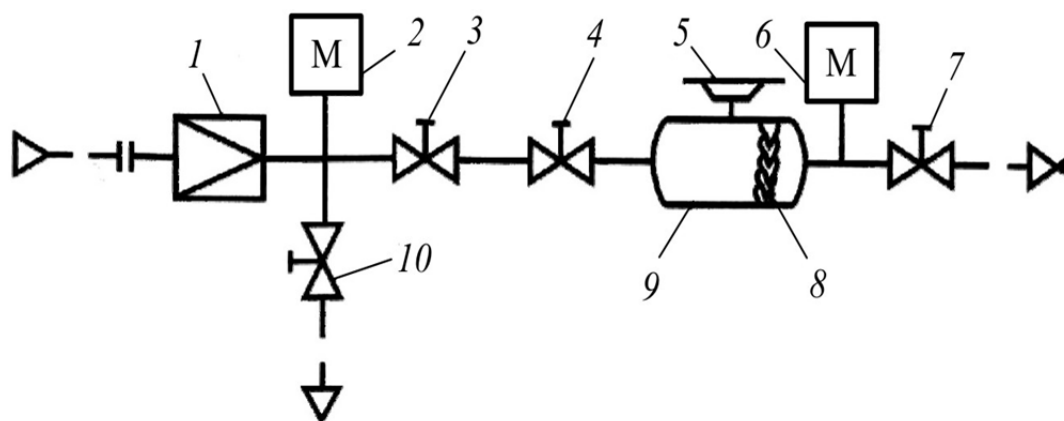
Схема контролю зварних з'єднань методом падіння тиску: 1 — редукторний клапан; 2 — манометр регулювання редукторного клапана; 3 — вентиль заповнення; 4 — запобіжний клапан; 5 — клапан повітряний автоматичний; 6 — контрольний манометр; 7 — вентиль скидання тиску; 8 — зварний шов; 9 — виріб; 10 — клапан
